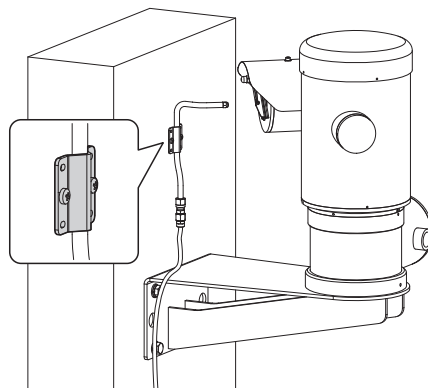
Tubo fissato alla parete tramite la piastrina.
